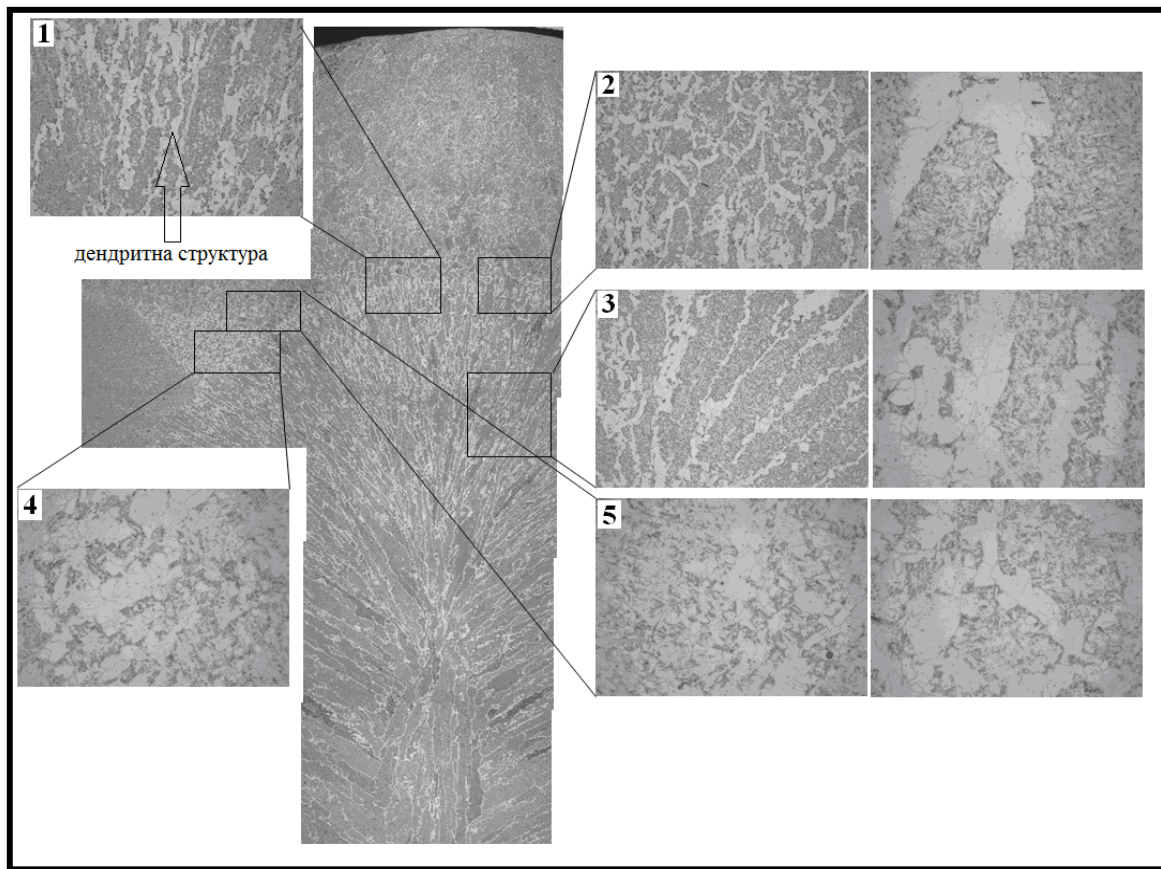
Загальний вид та будова структури зварного з'єднання після зварювання під шаром флюсу: сталь 10Г2ФБ: 1,2,3 – зона I; 4,5 – зона II [1].
